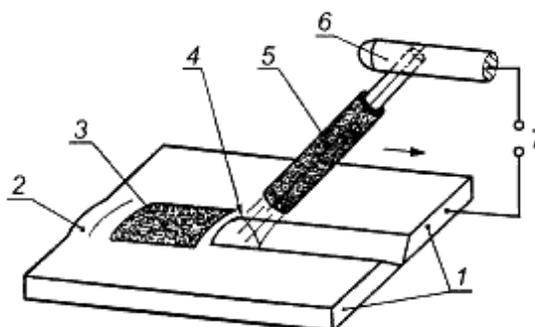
Схема ручной дуговой сварки
